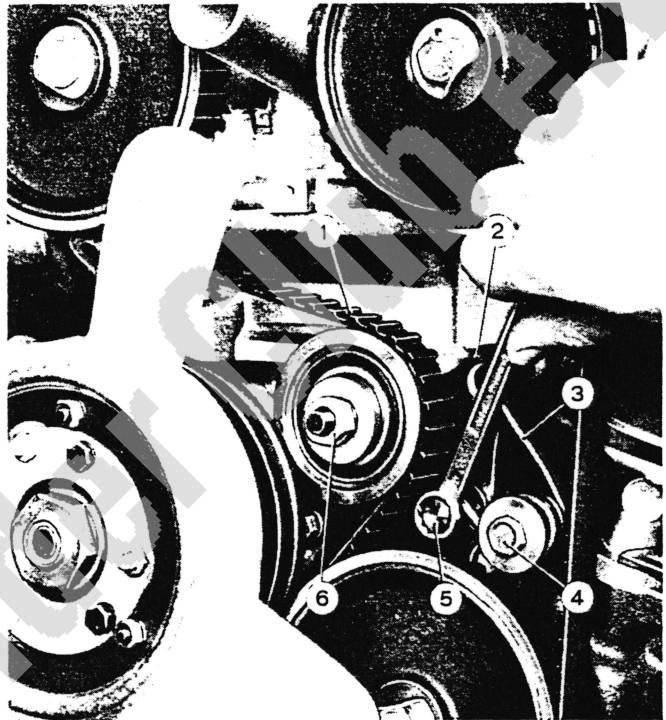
Befestigung der Gelenkschraube für Riemenpanner.
